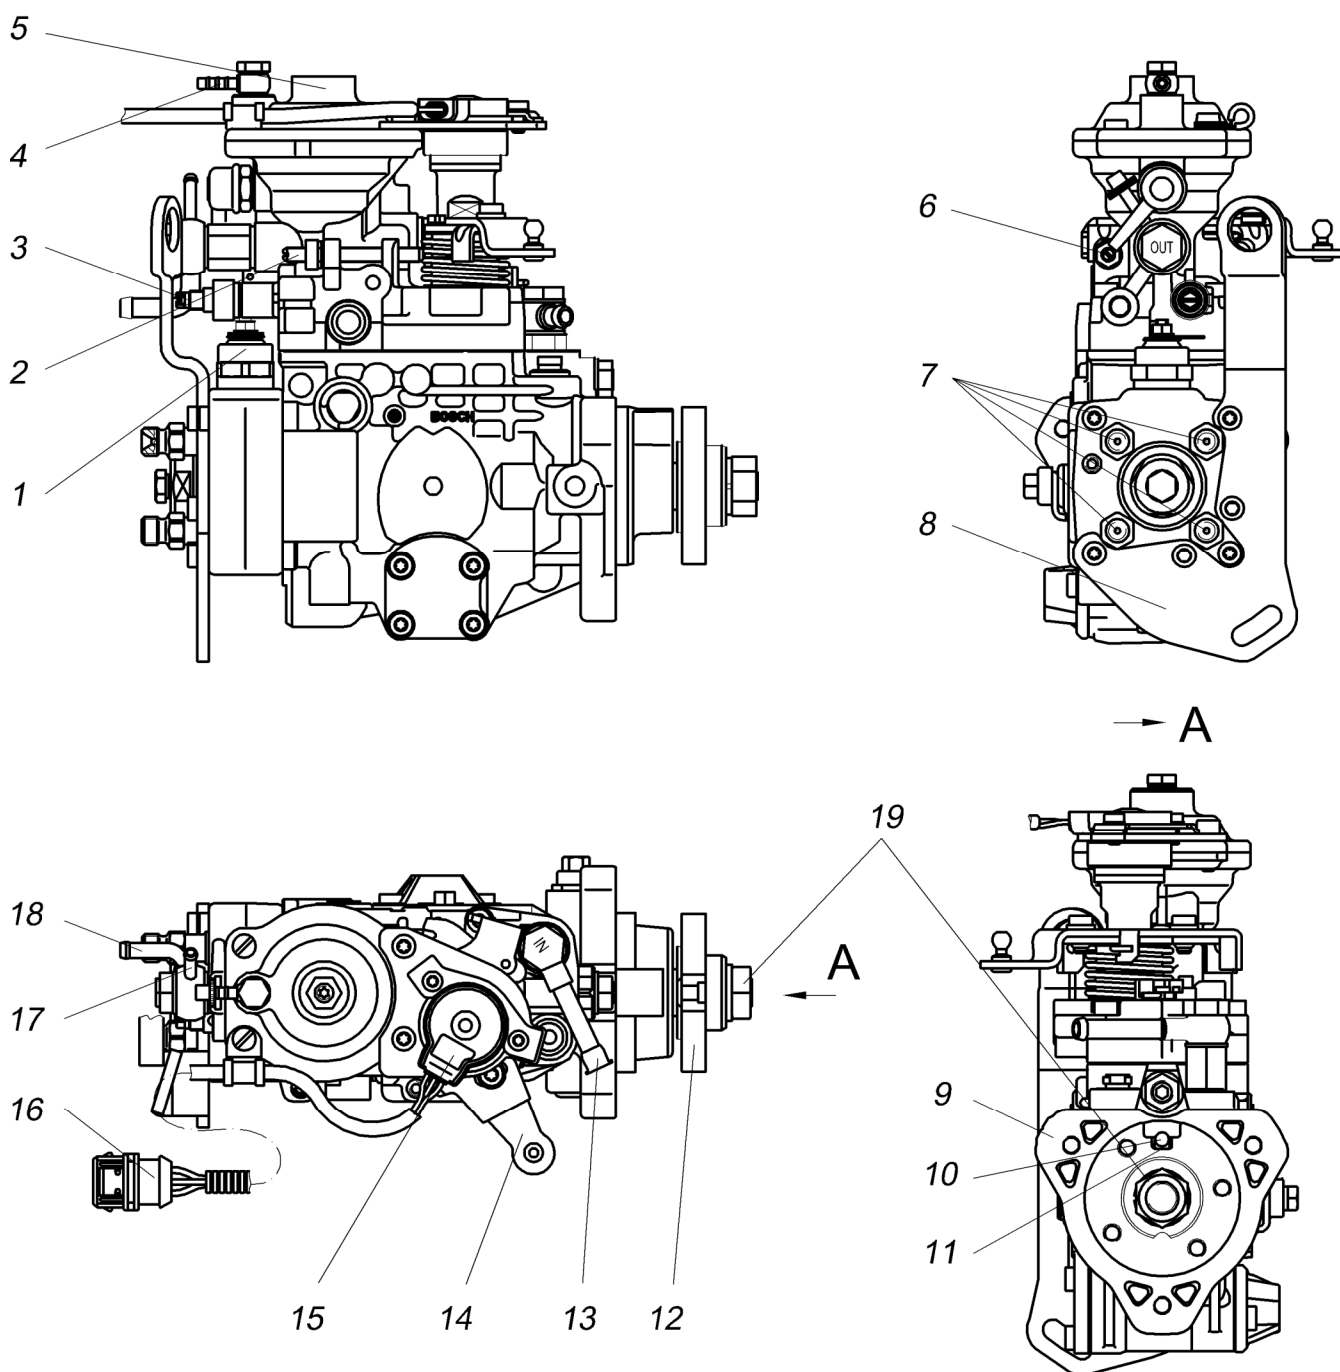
Топливный насос высокого давления BOSCH типа VE:
